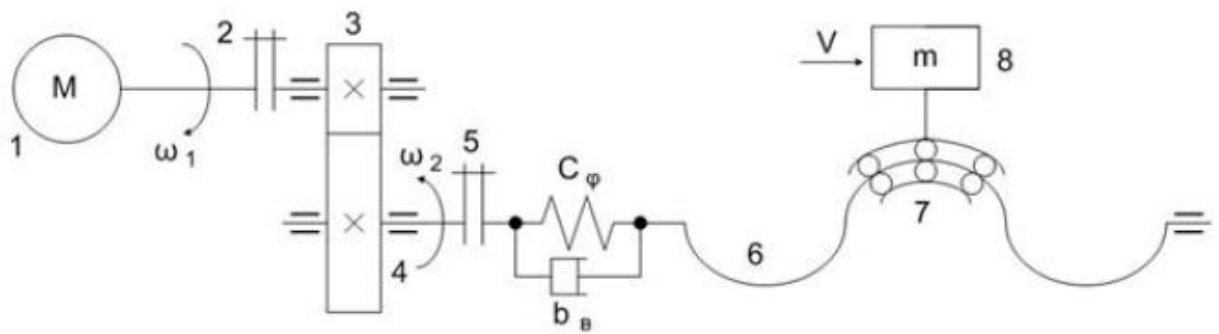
Кінематична схема механізму металорізального верстата 1 – двигун, 2 – муфта, 3, 4 – зубчасте колесо; 2, 5 – муфта, 6 – черв'як, 7 – гайка, 8 – стіл
